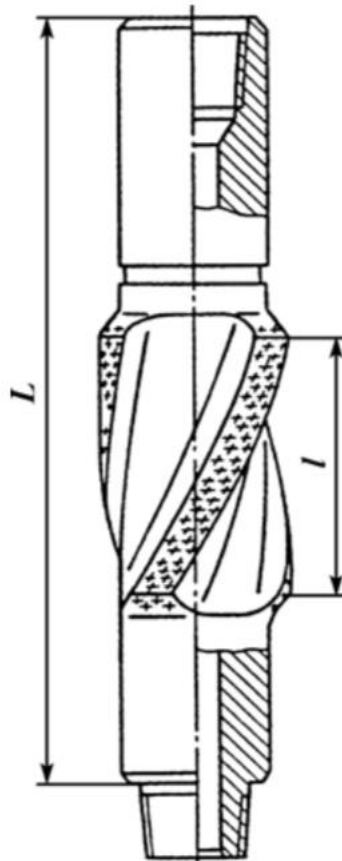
Колонный центратор со спиральными лопастями для роторного бурения
